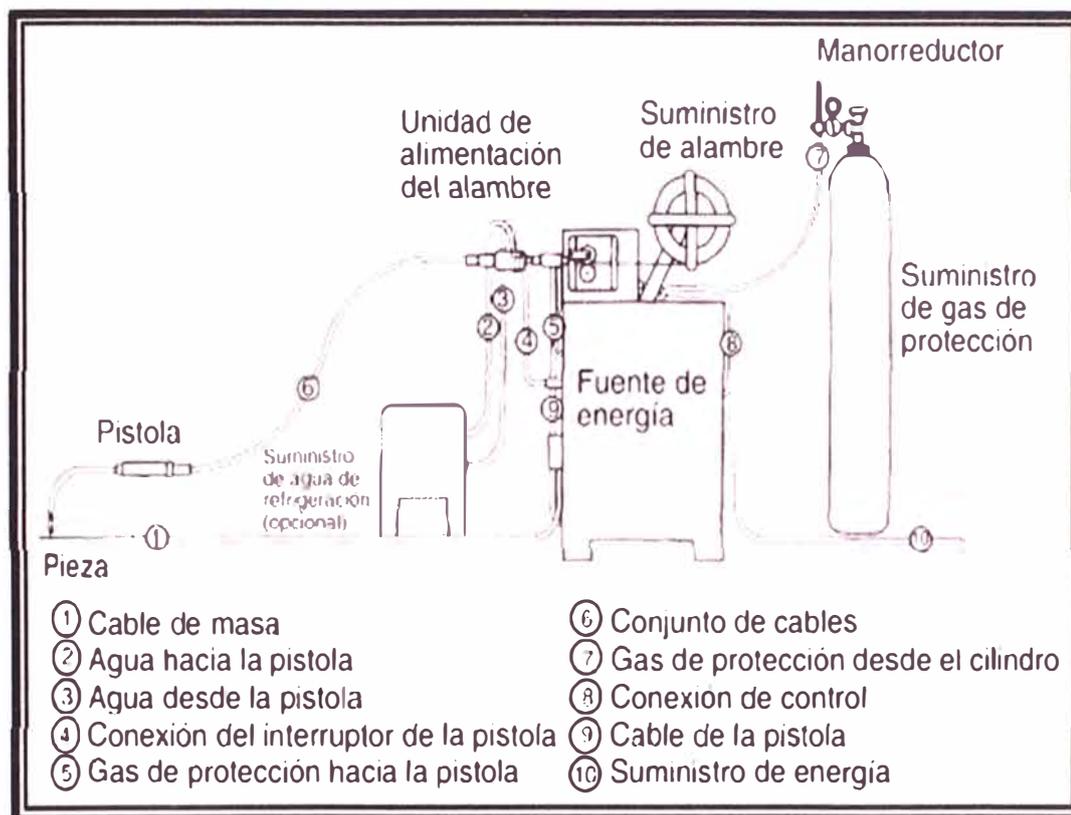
Esquema de un Equipo para la Soldadura Automática
